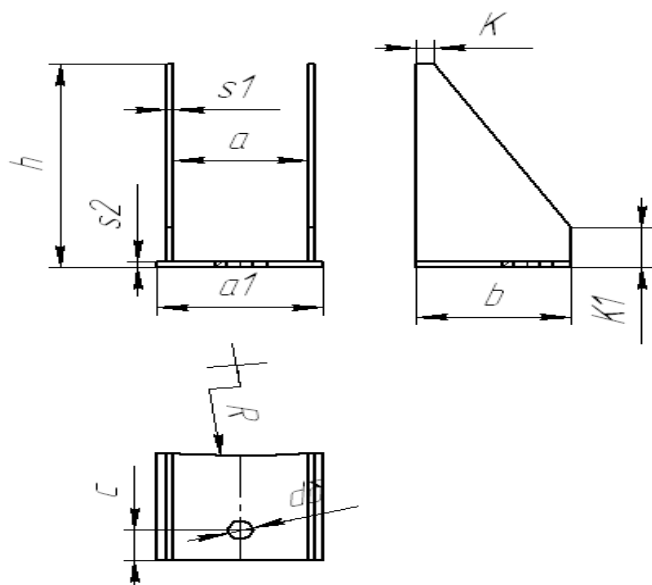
Стандартная опора для стальных сварных вертикальных цилиндрических аппаратов.
